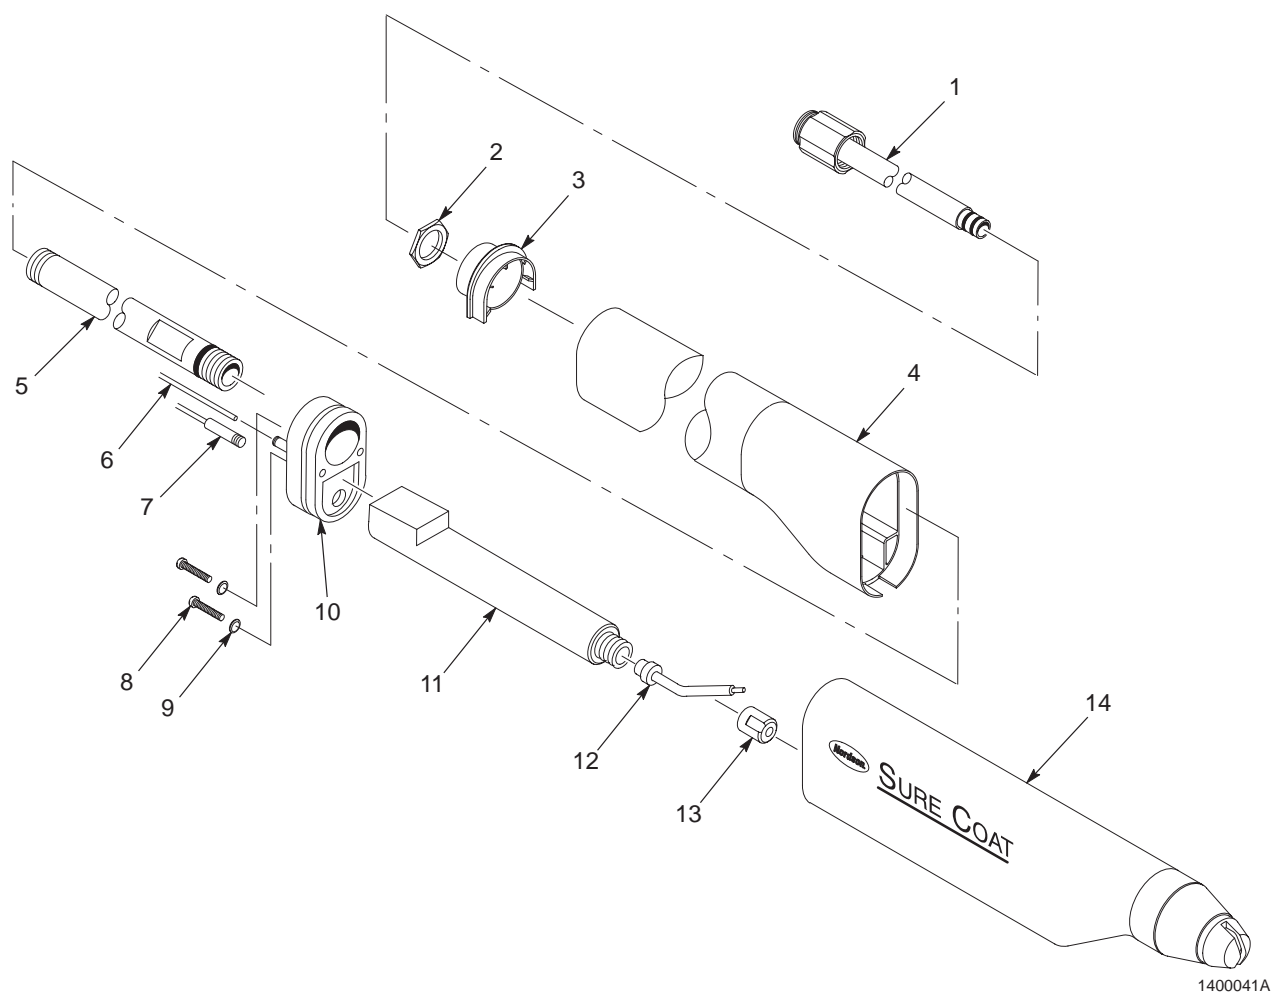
Remplacement du multiplicateur du pistolet à fixation par tube
